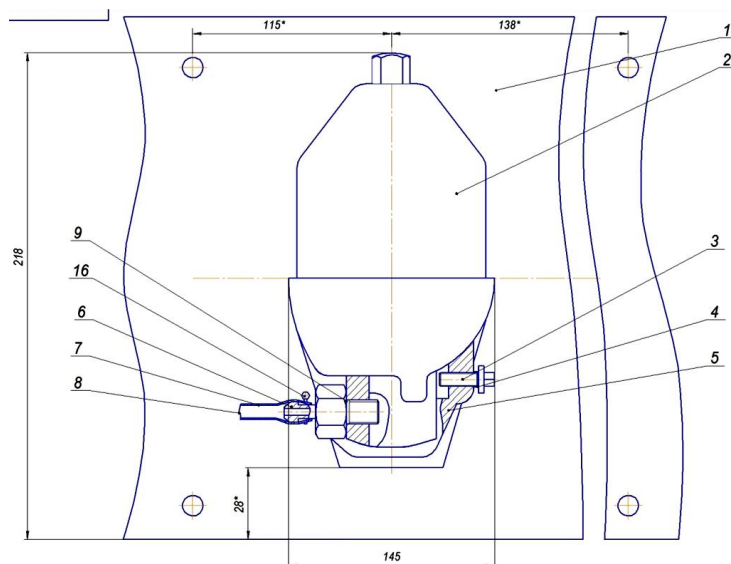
Розміщення фільтра на корпусі коробки передач: 1 – корпус; 2 – фільтр; 3 – пробка; 4 – прокладка; 5 – кришка; 6 – штуцер; 7 – арматура; 8 – шланг; 9 – прокладка.
